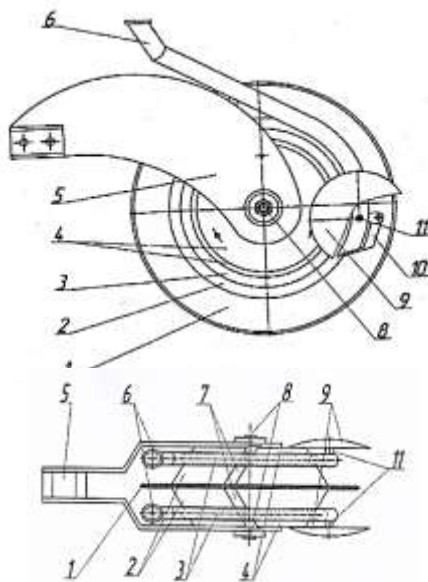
Комбинированный однодисковый сошник с двухсторонними ребрами и сферическими дисковыми загортачами для узкорядного посева: а – вид сбоку; б – вид сверху;
